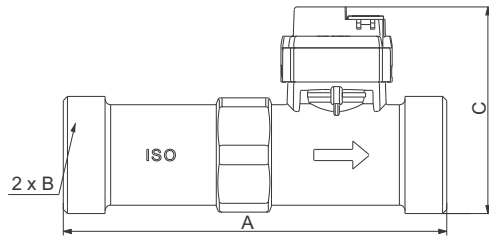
Abmessungen des Sensors MFS QT 20-200 l/min (mit Gewinde)
